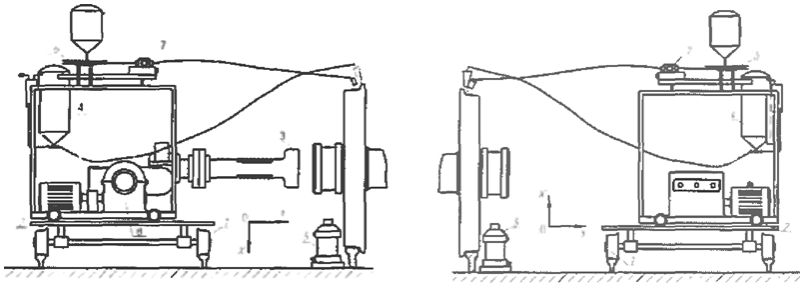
Установка для наплавлення гребенів колісних пар без викатки
